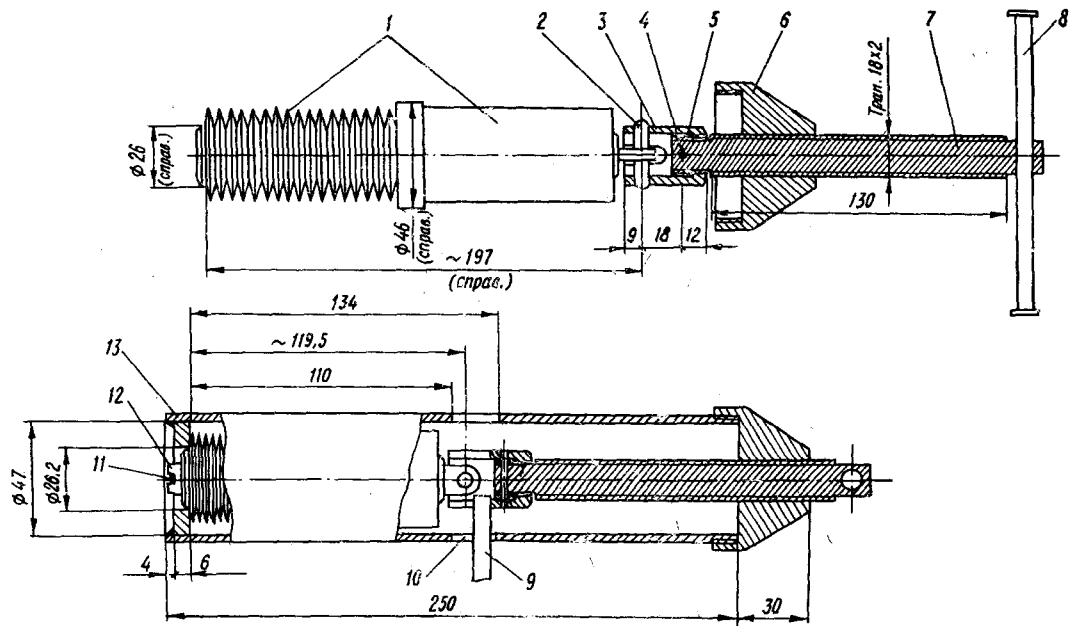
Приспособление для переборки пружинного амортизатора Ш4700-20 лыжонка (Ст. 45):
